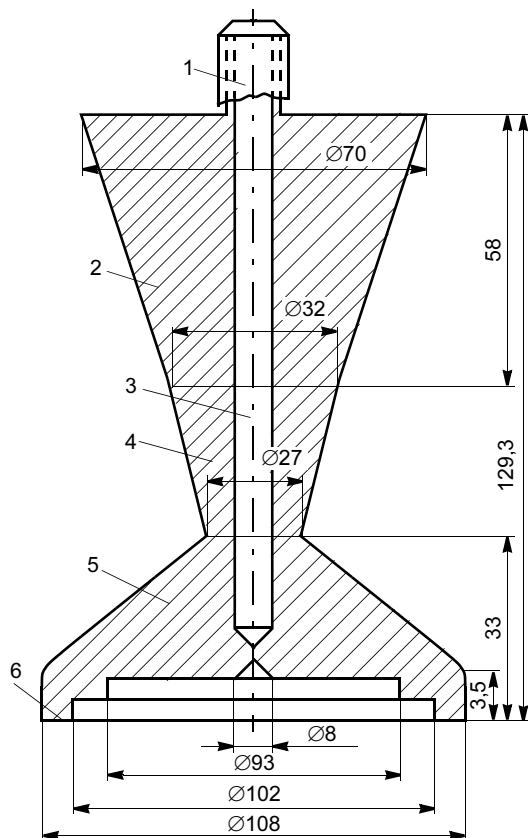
Общий вид контурного волновода для сварки изделий из термопластов: 1 — резьбовое соединение; 2 — стержень; 3 — аксиальный канал для охлаждения; 4 — ножка; 5 — демпфирующая масса; 6 — рабочая поверхность
